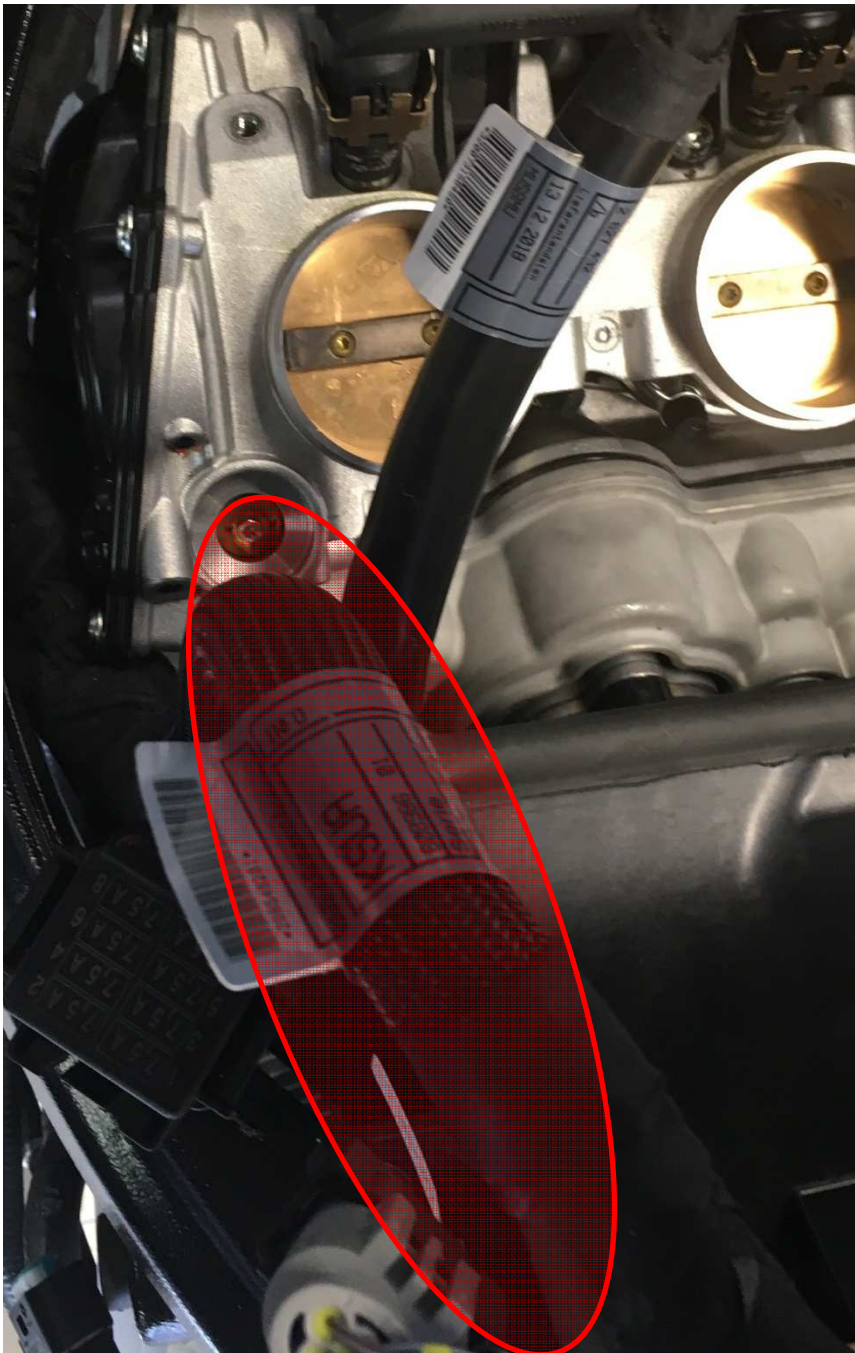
Le brin principal du faisceau se profile le long droit de la boîte à air et dans la poutre droite du cadre principal.
